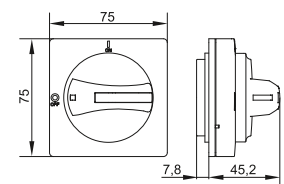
Габаритные размеры поворотной рукоятки / Figure 2 – Overall dimensions of rotary handle
